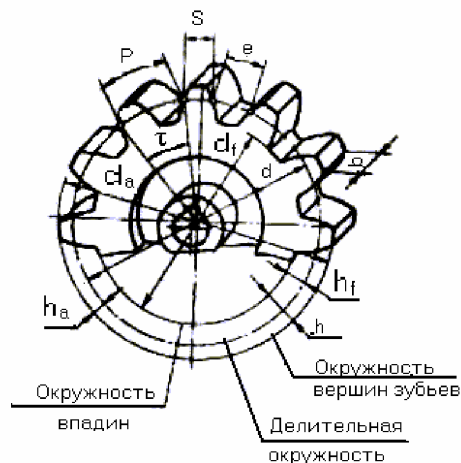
Шестерня (ГОСТ 1643-72)
